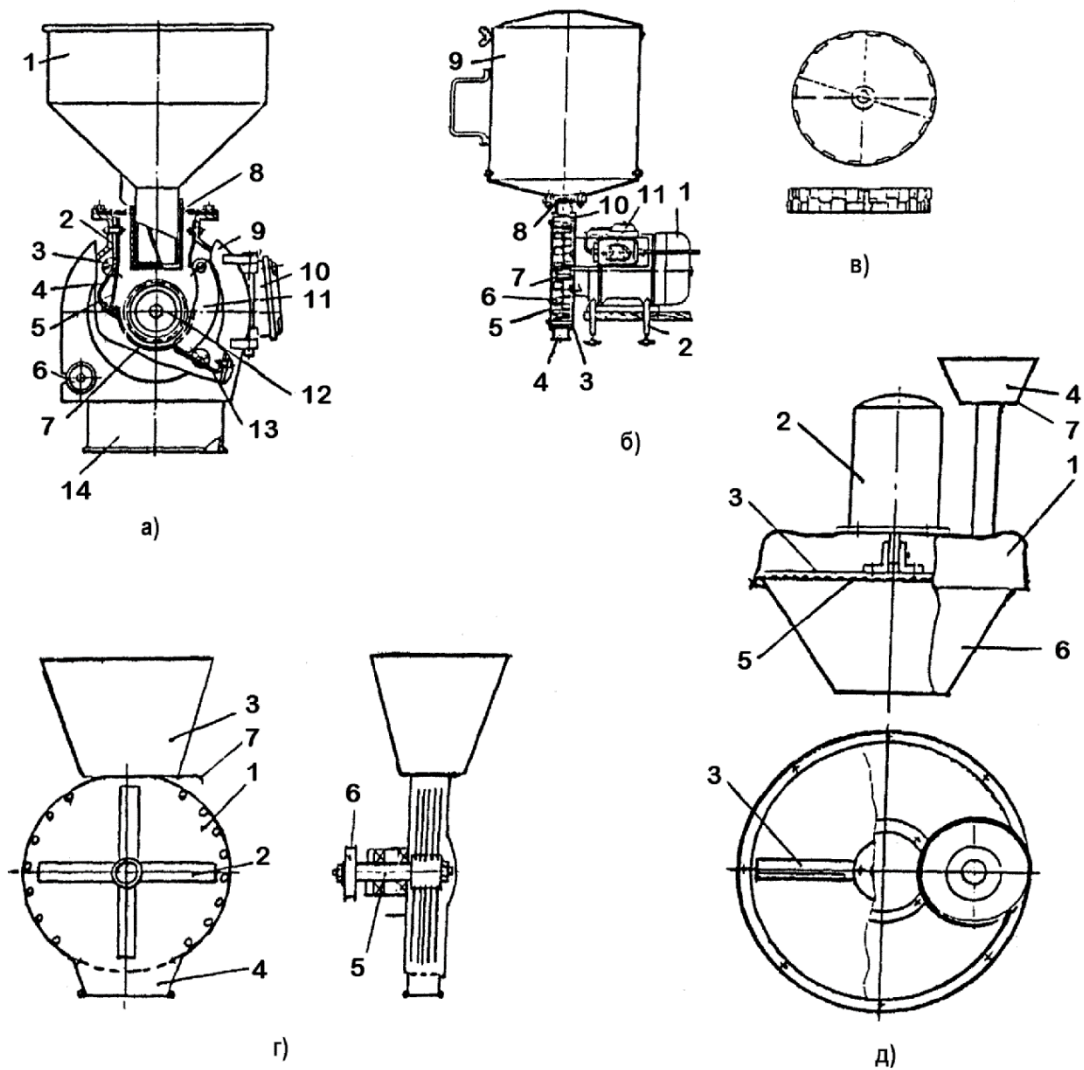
Конструктивні схеми дробарок з жорстким кріпленням робочих органів: а) МКД-Ф: 1- завантажувальний бункер; 2- корпус; 3- гвинт; 4,5,13-пластини; 6- гайка-маховичок; 7- змінне решето; 8- вставка; 9- кришка; 10- пусковий пристрій; 11- дека; 12- ротор; 14- вивантажувальна горловина. б) ЕЗД-Т-1: 1- електродвигун; 2- струбцина; 3- корпус дробильної камери; 4- вивантажувальний патрубкок; 5- кришка; 6- ротор; 7- ступиця; 8- засувка; 9- циліндричний бункер; 10- дека; 11- пусковий пристрій. в) робочий орган ЕЗД-Т-1. г) 1- дробильна камера; 2- жорстко закріплені молотки; 3- завантажувальний бункер; 4- вивантажувальна горловина; 5- вал дробарки; 6- шків; 7- регулювальна засувка. д) 1- корпус дробарки; 2-двигун; 3- ніж; 4- бункер; 5- решето; 6- вивантажувальна горловина; 7- регулювальна засувка
